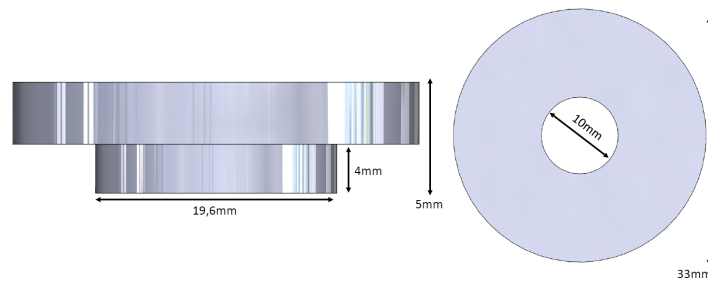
Vue 3D et dimensions globales du bouchon de la chambre à perfusion.
